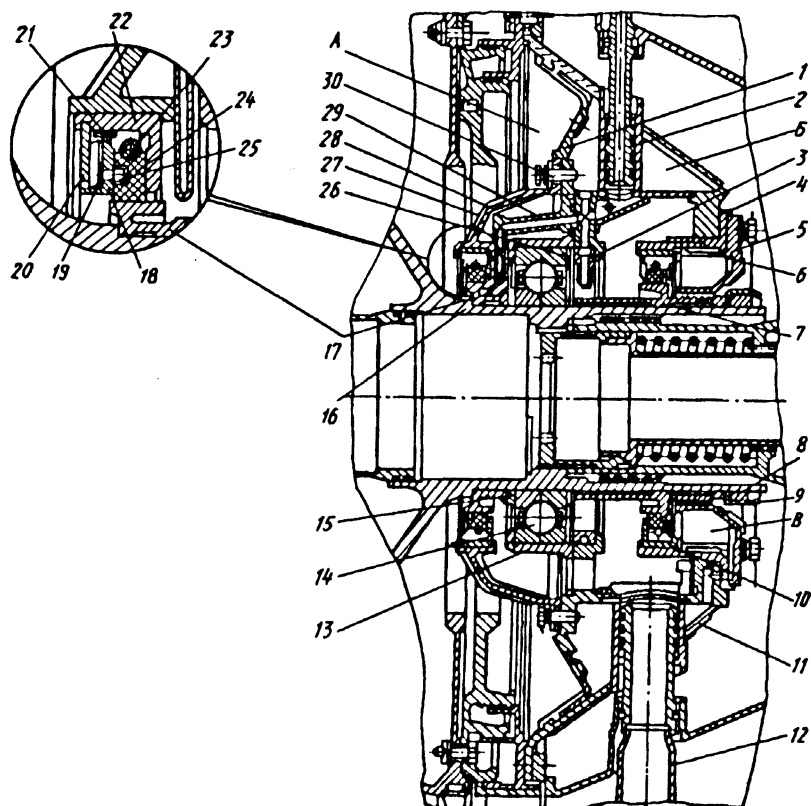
Задняя (вторая) опора ротора компрессора:
